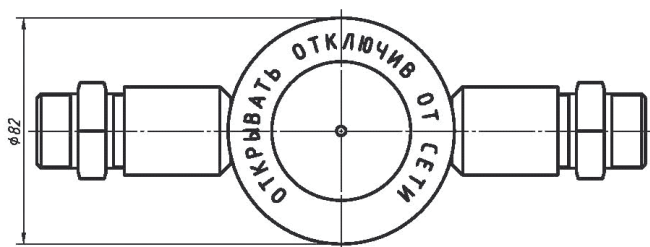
Извещатель ИП103-1В с головкой из стали 12Х18Н10Т, кабельные вводы для трубной прокладки кабеля (вариант кабельного ввода – для прокладки бронированного кабеля)
